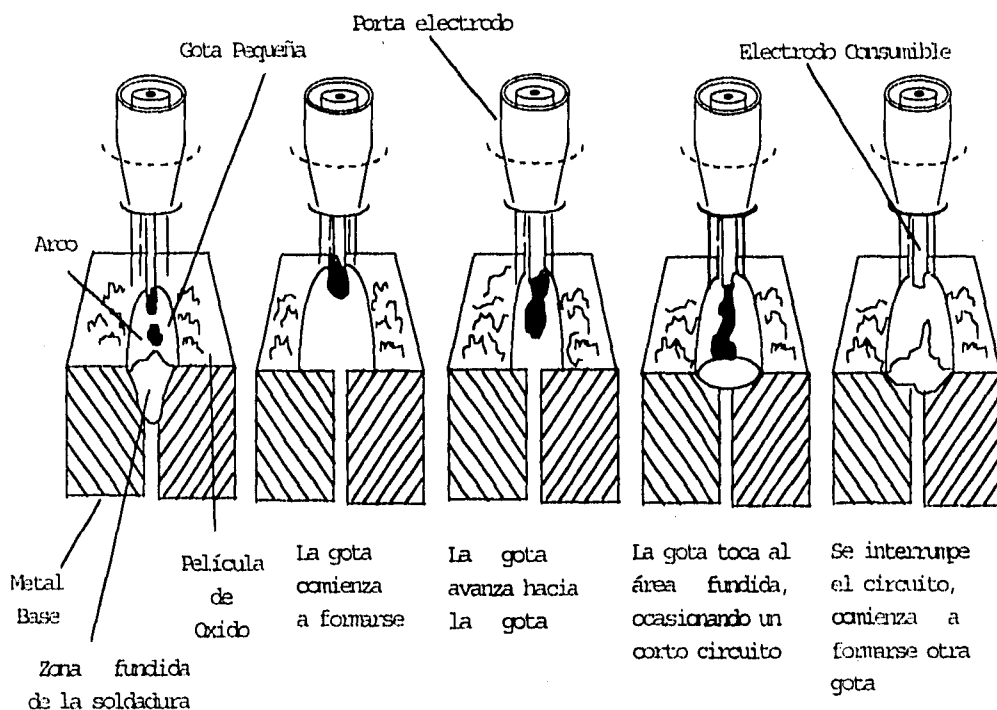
Métodos de transferencia del metal en la soldadura de arco metálico y gas en el caso del método de soldadura MIG.
